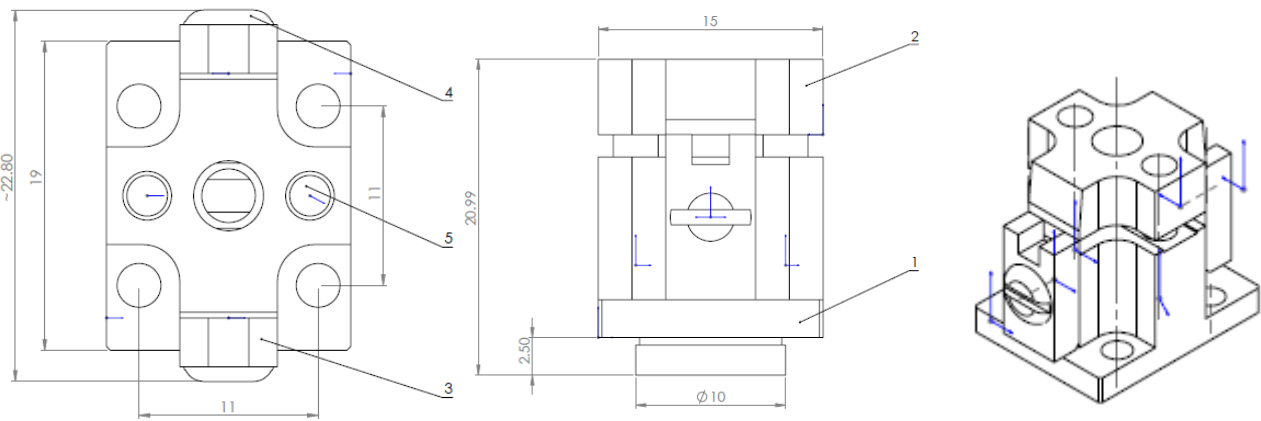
Componentă de prindere din sistemul de orientare a probeleor
